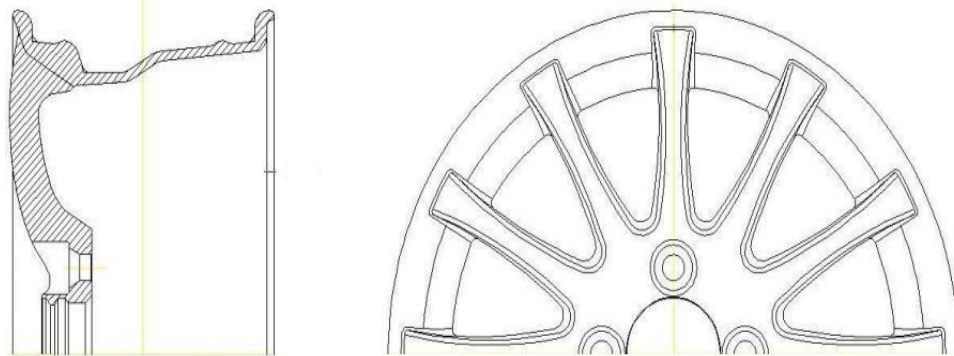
Схема різання заготовок зразків для контролю механічних властивостей і хімічного складу серійних колес
